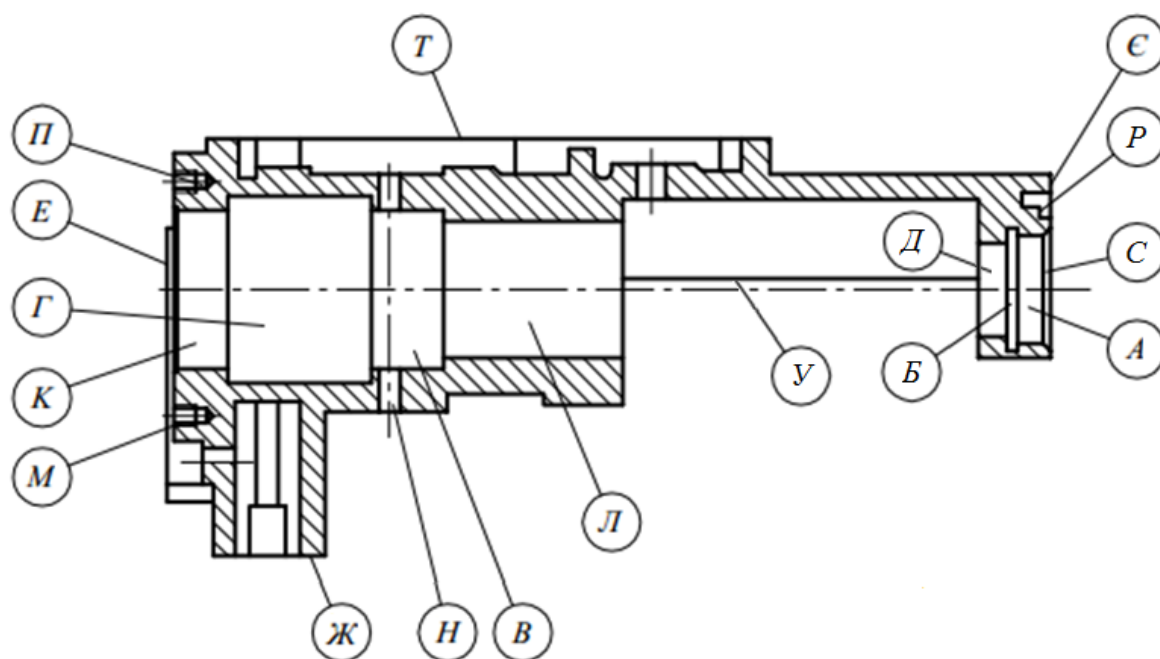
Загальний вид корпусу Т 001.709
